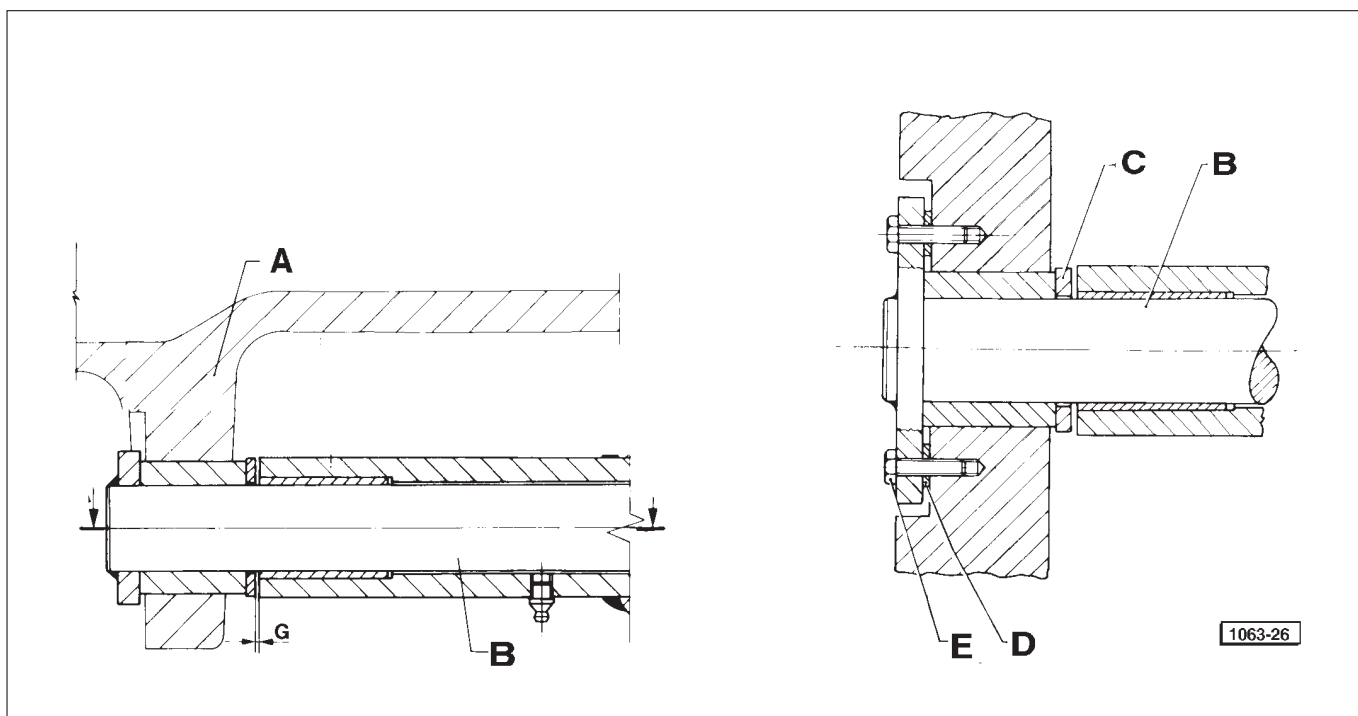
Réglage du jeu axial de l'essieu avant.
